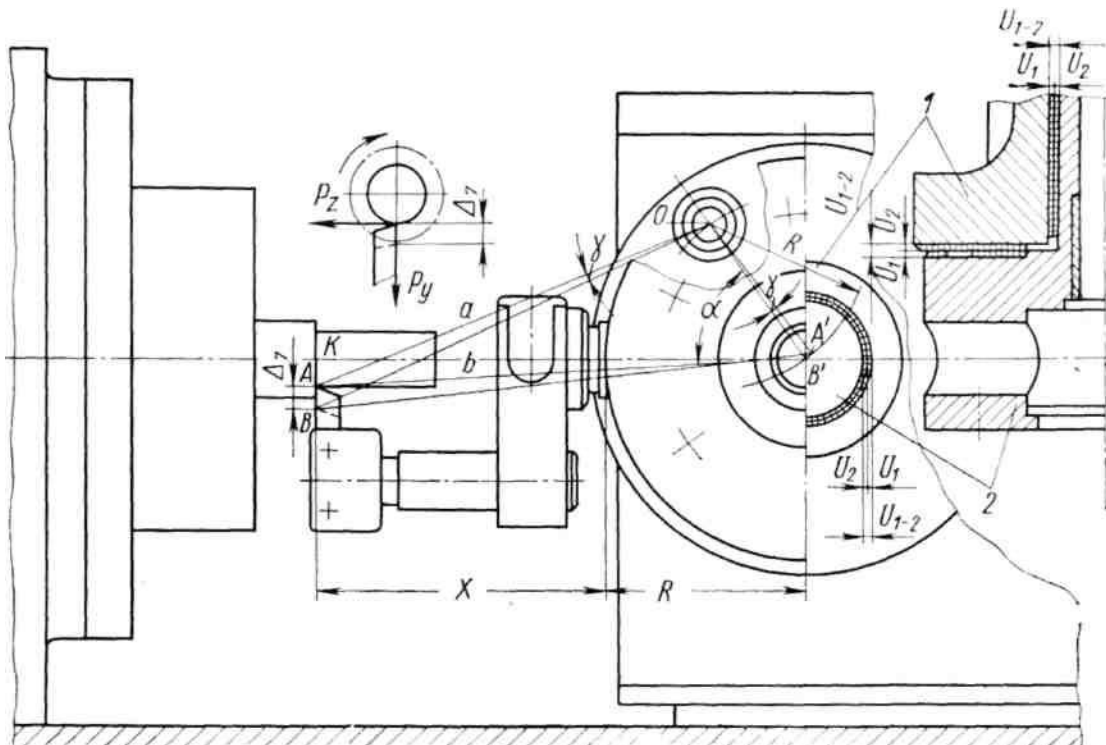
Схема визначення похибки обробки від сполучення корпус револьверного супорта - револьверна головка (знос по посадочних шийках): 1 - корпус револьверної головки; 2 - револьверна головка
